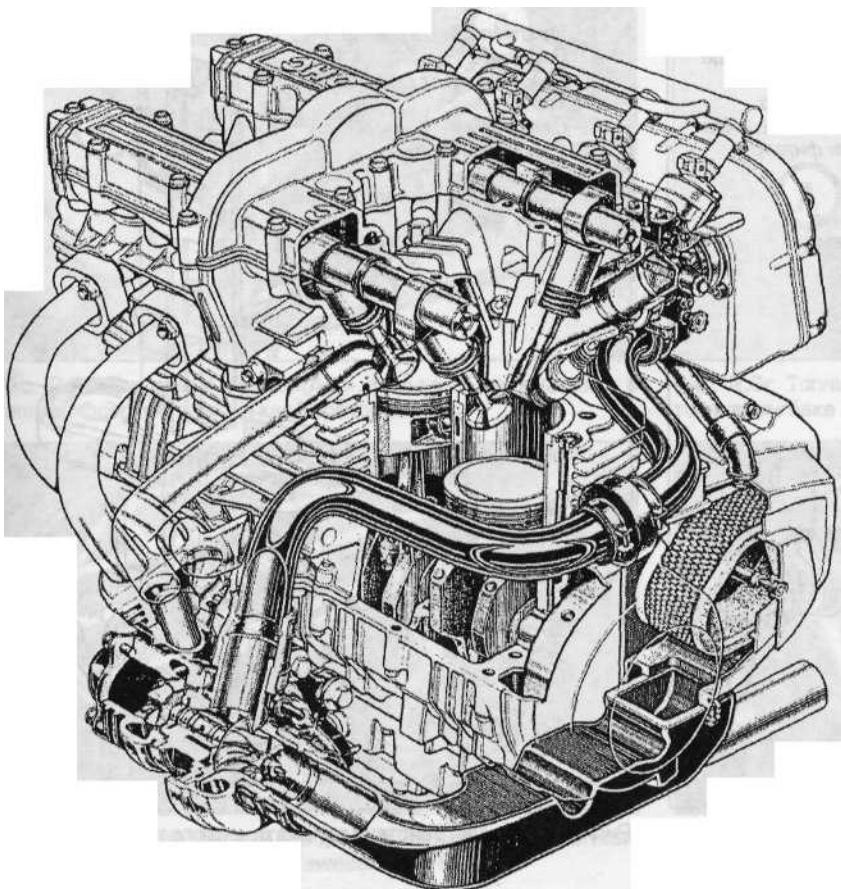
Разрез двигателя Kawasaki ZX750T
